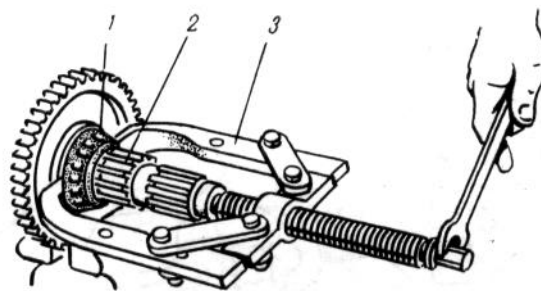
Випресування внутрішнього кільця підшипника з вторинного вала: 1- внутрішнє кільце; 2- вторинний вал; 3- знімач
